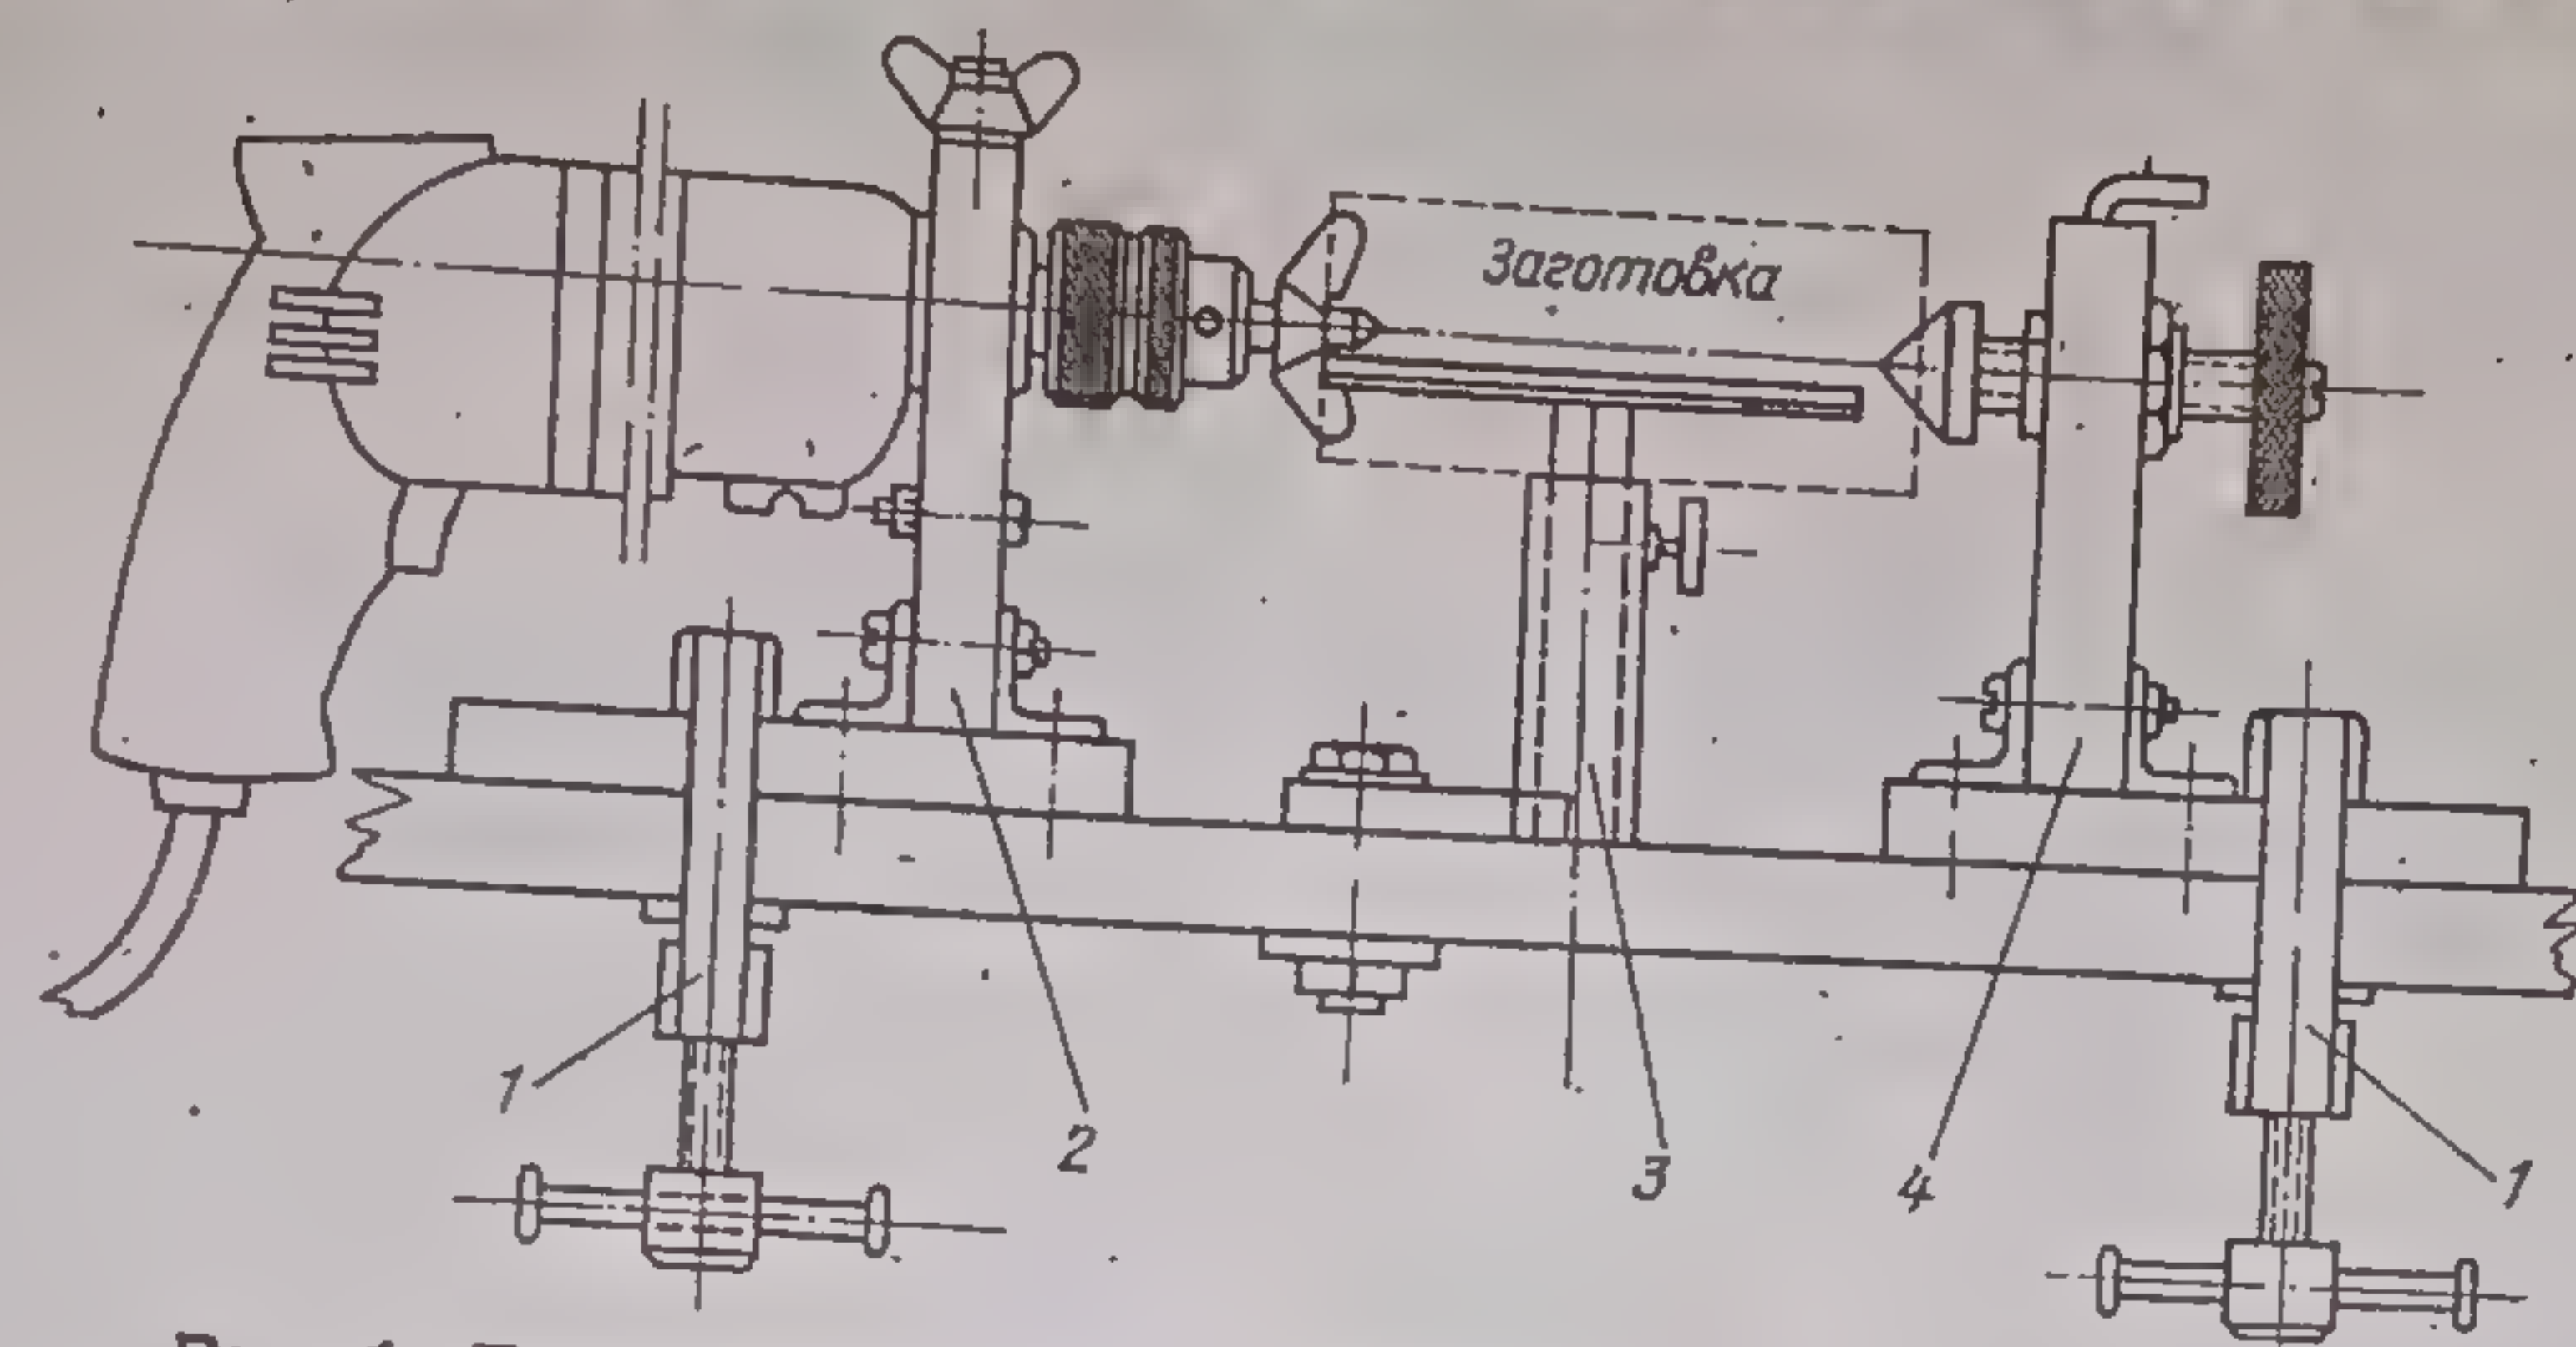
Токарный станок на основе электродрели: 1 — струбцина; 2 — передняя бабка; 3 — упор для резца; 4 — задняя бабка.
